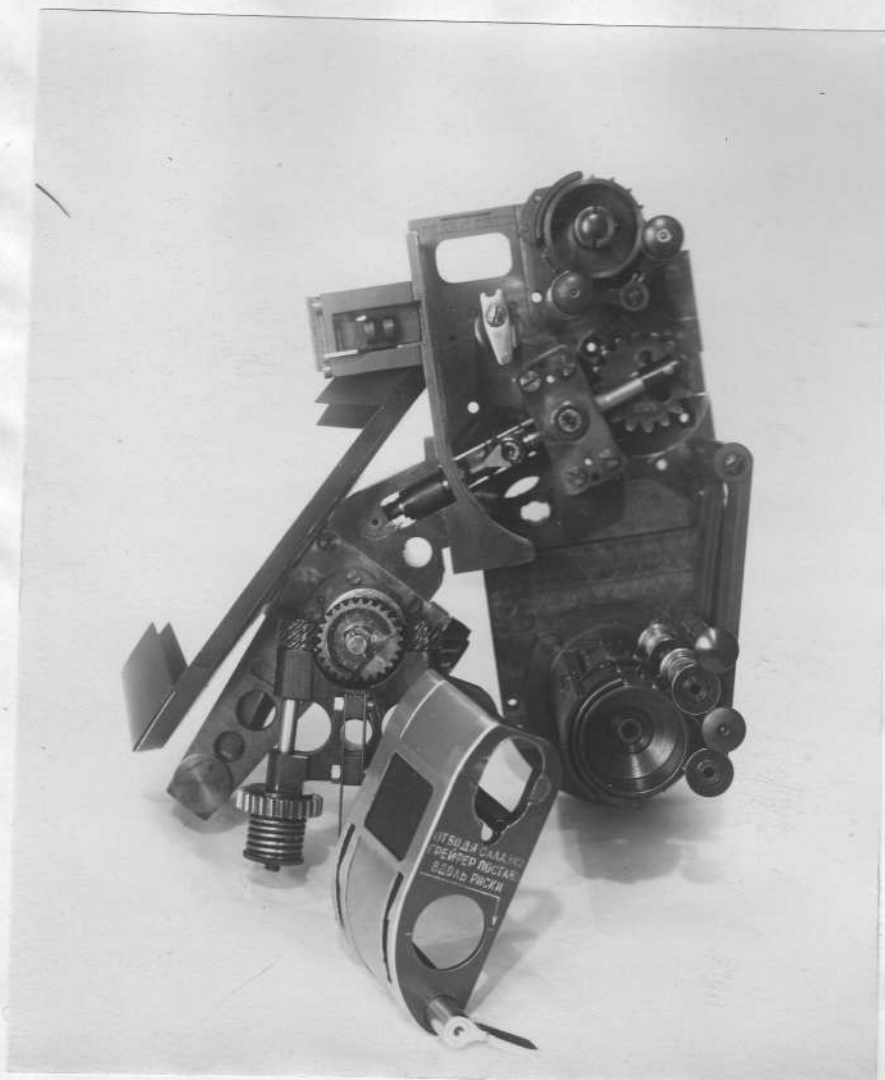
Грейферный механизм со снятыми задними салазками для протирки фильмового канала.
